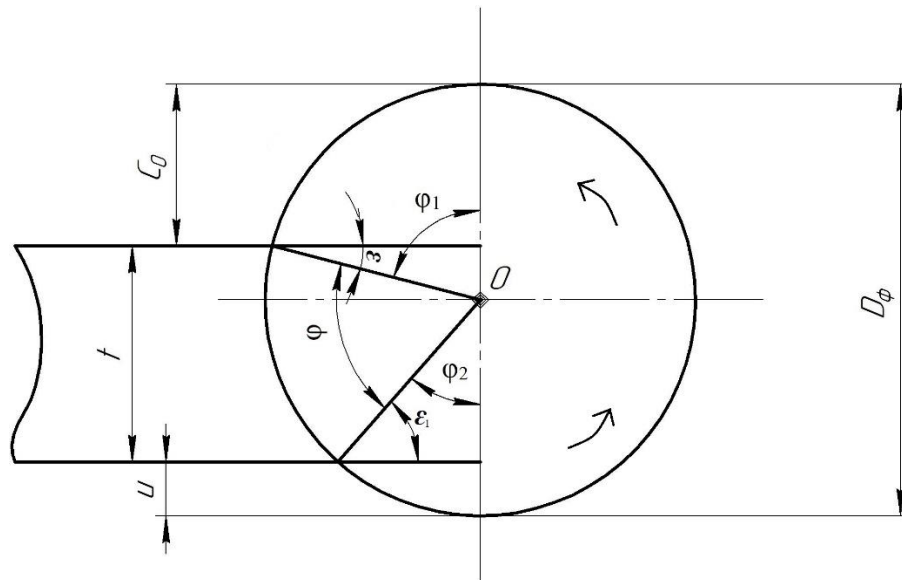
Схема расположения заготовки относительно торцевой фрезы.
